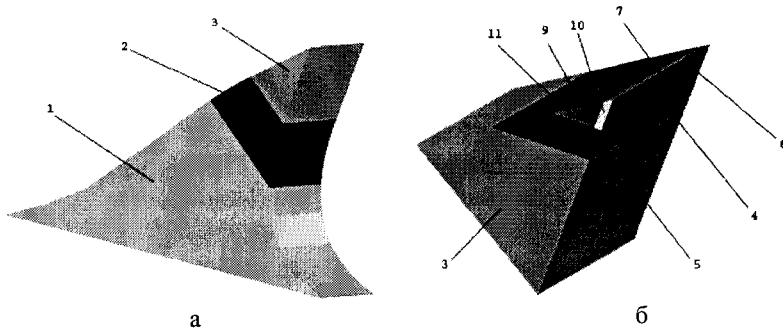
Твердотільна модель розведеного зубця стрічкової пилки першого типу: а - зубець; б - верхня частина зубця.
